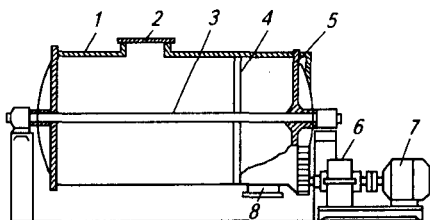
Аппарат для гашения извести: 1 — барабан; 2, 8 — люки; 3 — вал; 4 — перегородка; 5 — шестерни; 6 — редуктор; 7 — электродвигатель
